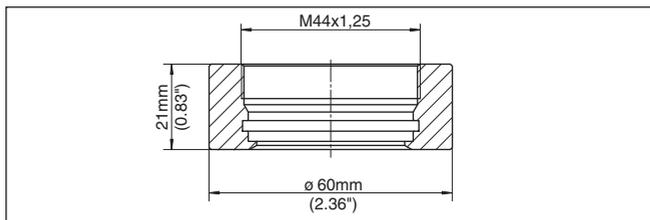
Dimensiones racor para soldar M44 x 1,25 - VEGABAR 82, 83
